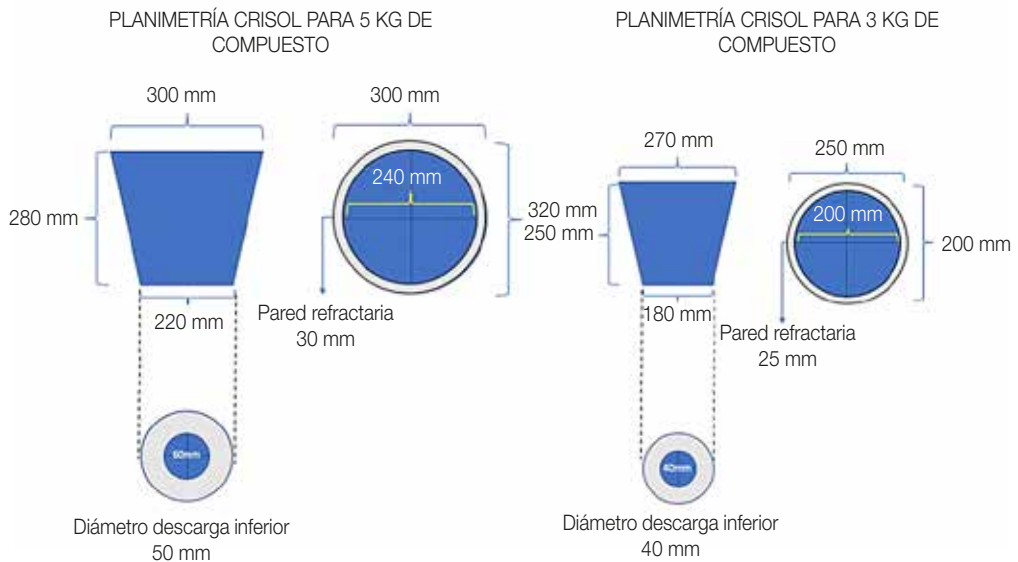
"Planimetría de detalle crisol 3 y 5 kg respectivamente".
